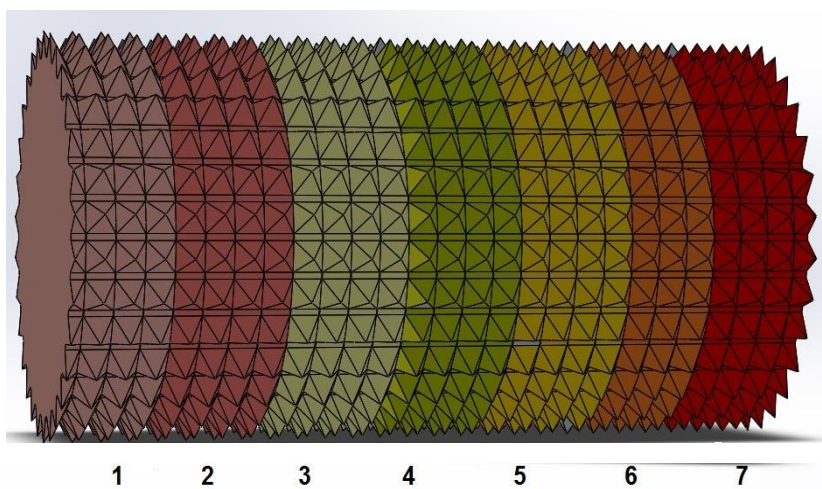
Disposición de soldaduras 2° maza superior
